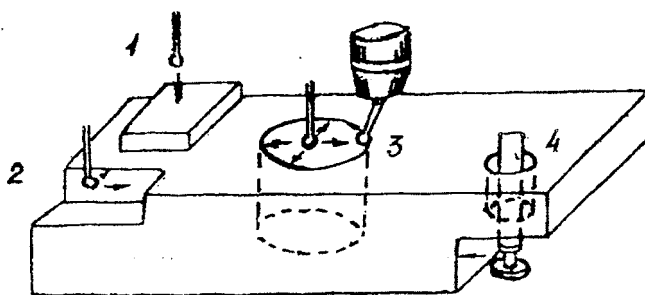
Схемы измерений обработанной заготовки щупами
